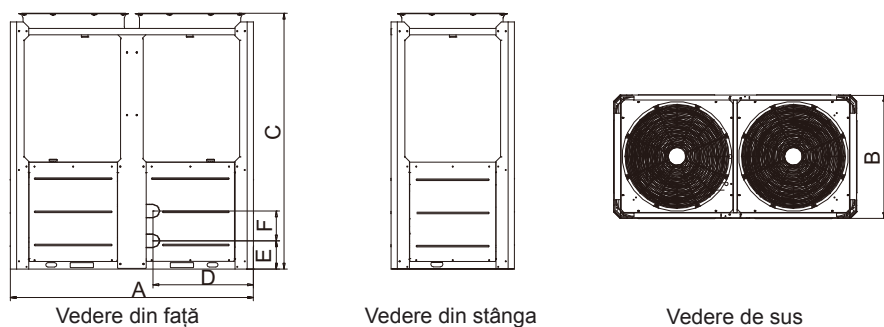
Schema dimensională a KEM-90 DRS5
